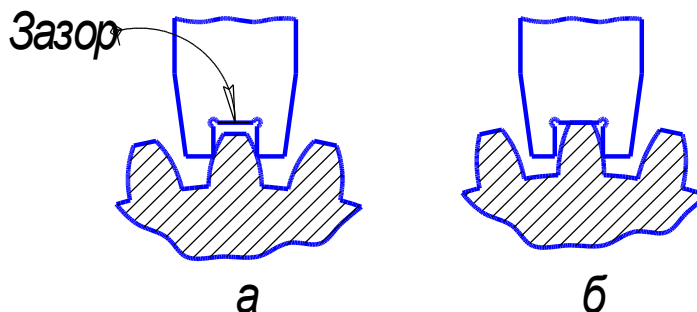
Проверка износов зубьев шестерни шаблоном:
